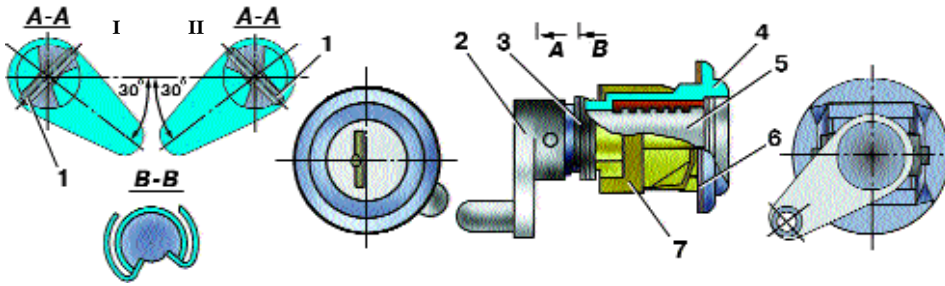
Выключатель замков передних дверей: 1 – штифты; 2 – поводок; 3 – возвратная пружина; 4 – корпус выключателя; 5 – цилиндр выключателя; 6 – прокладка; 7 – держатель; I – левая дверь; II – правая дверь
